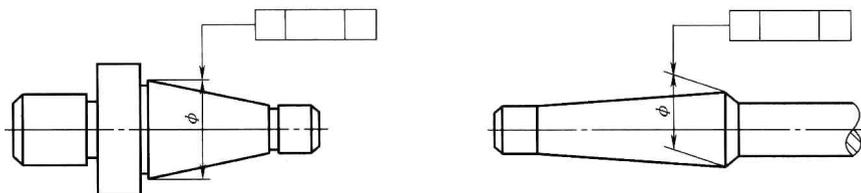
被测要素为圆锥体轴线时几何公差代号的标注
